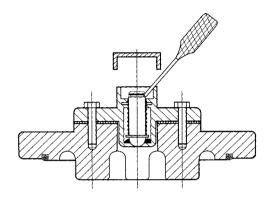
Схема выпуска воздуха через крышку устройства РПН
